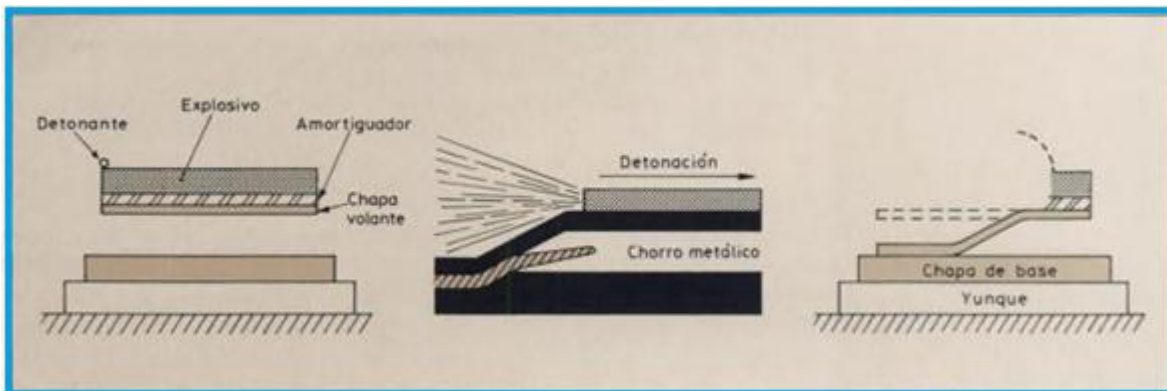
Zona de unión en una soldadura por explosión.
